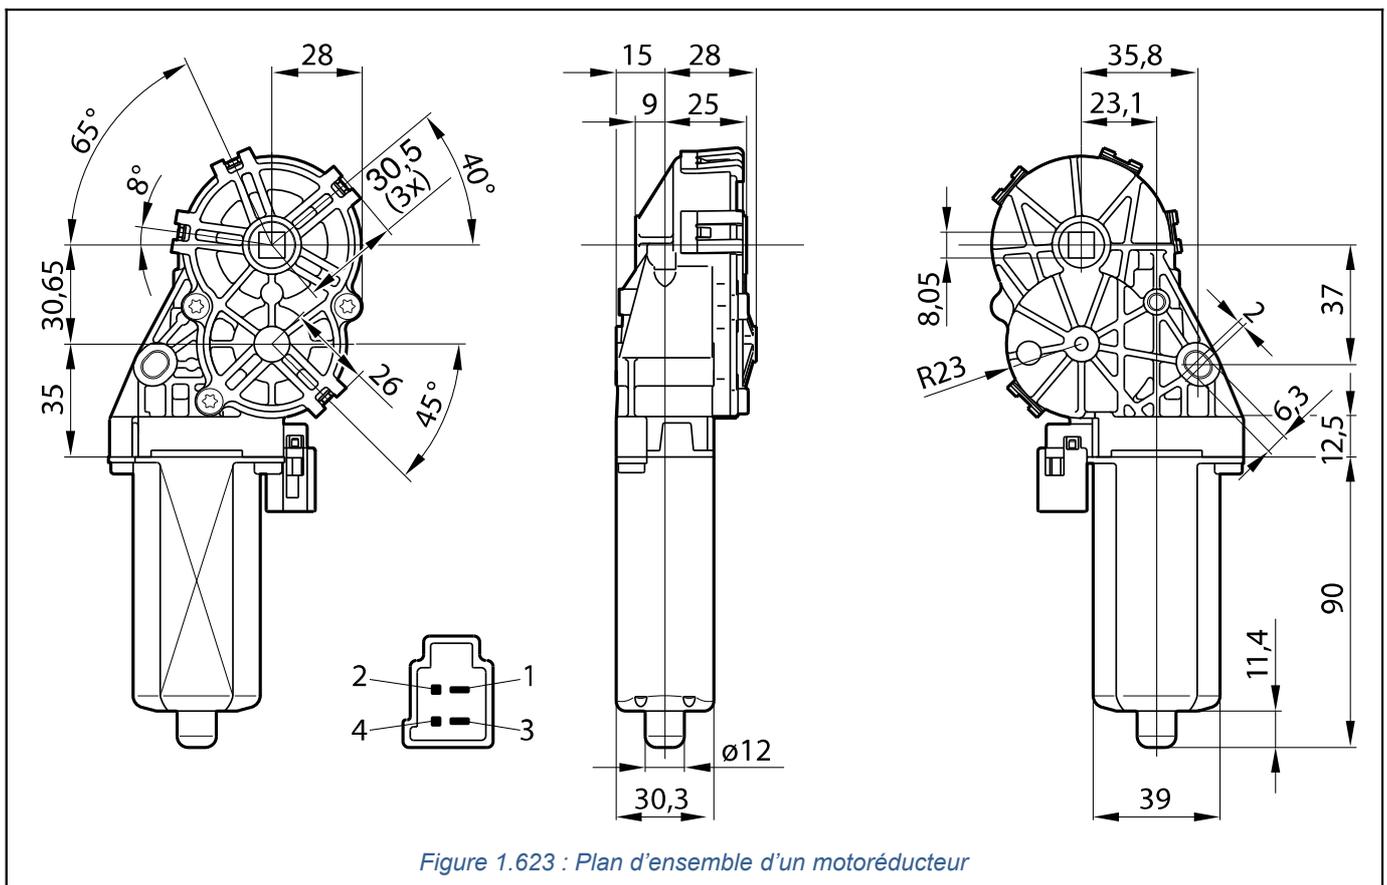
Plan d'ensemble d'un motoréducteur
